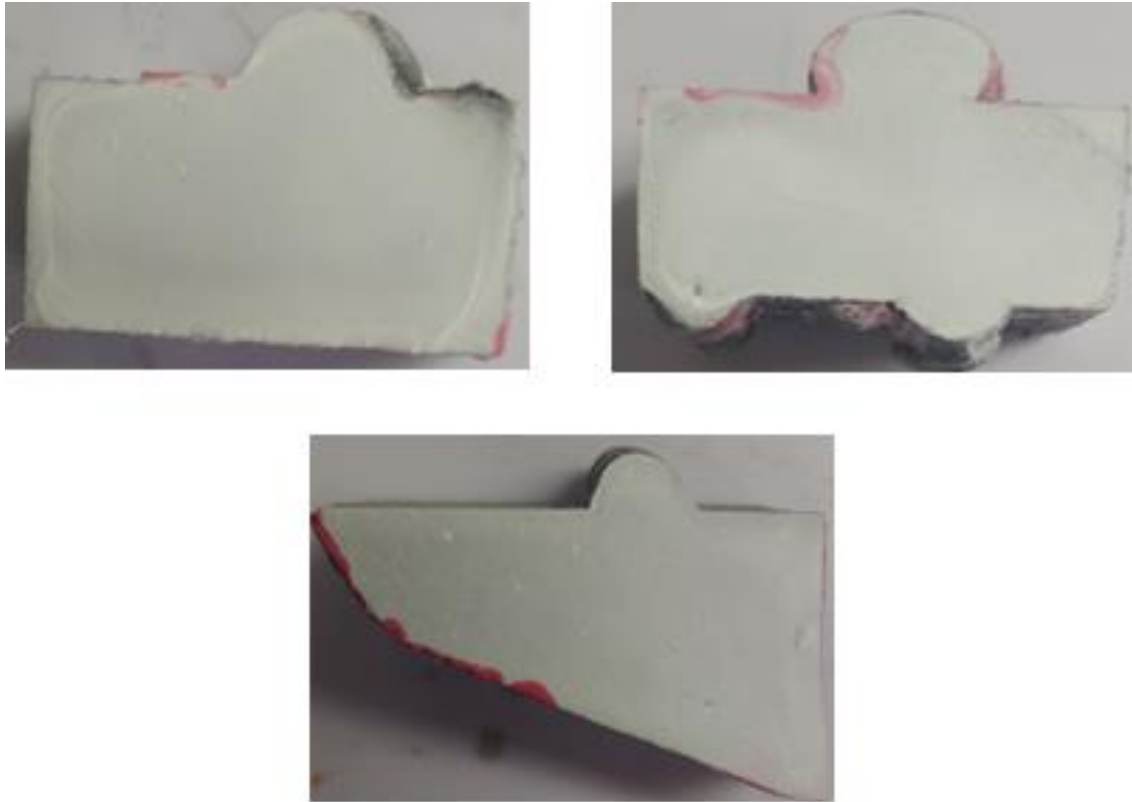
Inspección en cortes transversales de cordones con electrodo E-9018-B3.
